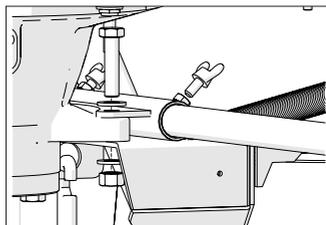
Visser le support de tuyau et fixer le support de malaxeur
